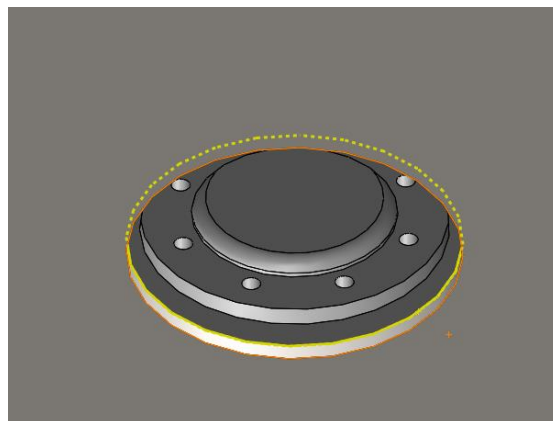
Detalle de soldadura de placa soporte King Pin
